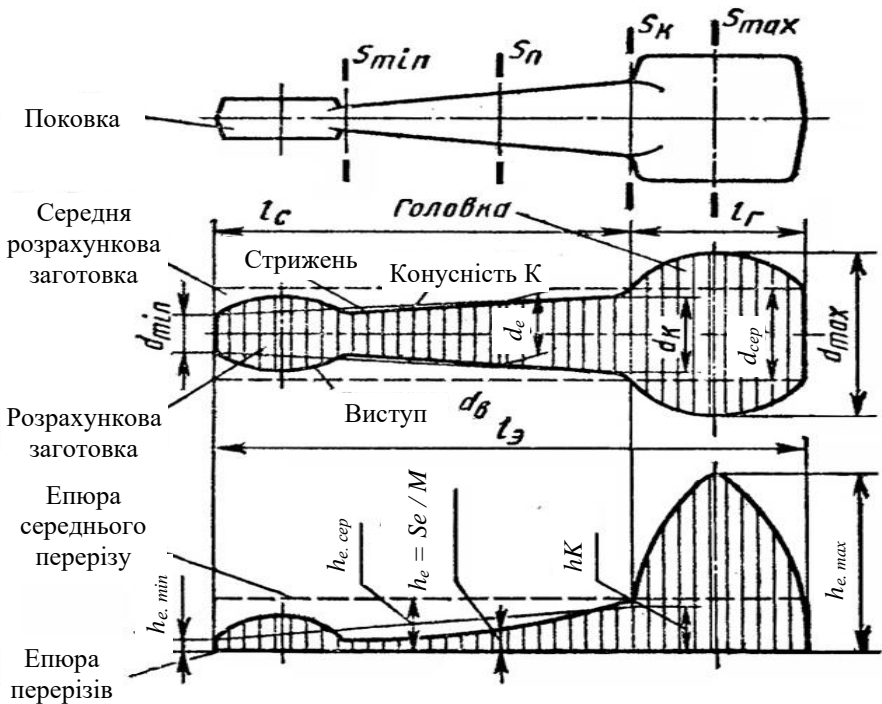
Елементарна розрахункова заготовка та еюра перерізів
